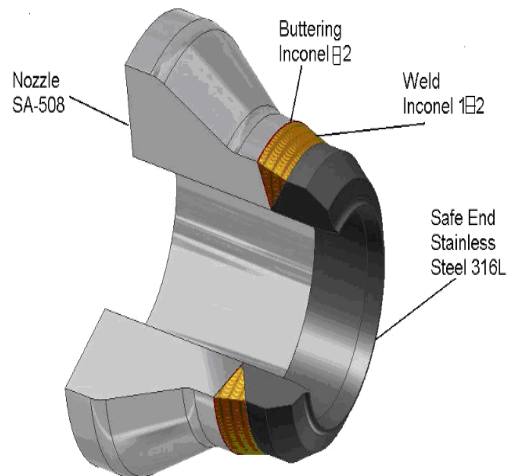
Boquilla con soldadura de aleación 82/182 a un extremo seguro (safe end). ⁽³⁴⁾
